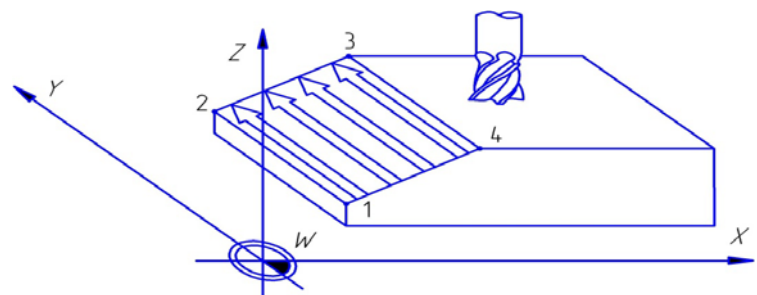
Фрезерование поверхности заготовки, наклонной к оси Y
